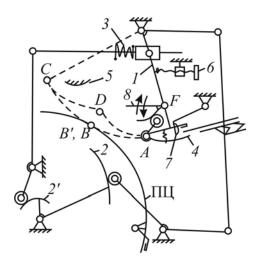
Схема механизма верхнего качающегося форгрейфера: 1 – рычаг форгрейфера; 2, 2′ – кулачки; 3 – пружина; 4 – створки захватов; 5 – неподвижная горка; 6 – регулировочные упоры; 7 – передние упоры; 8 – подвижная горка;  $\Pi \coprod$  – печатный цилиндр
